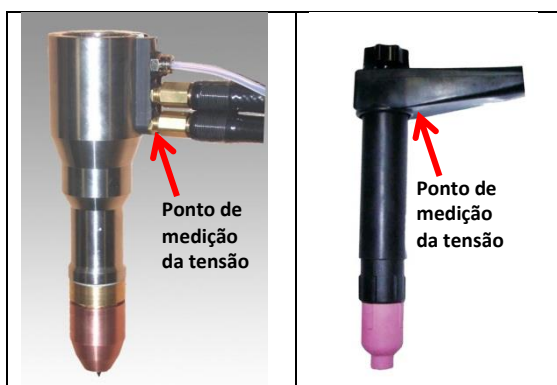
Pontos de medição da tensão do arco de soldagem.
